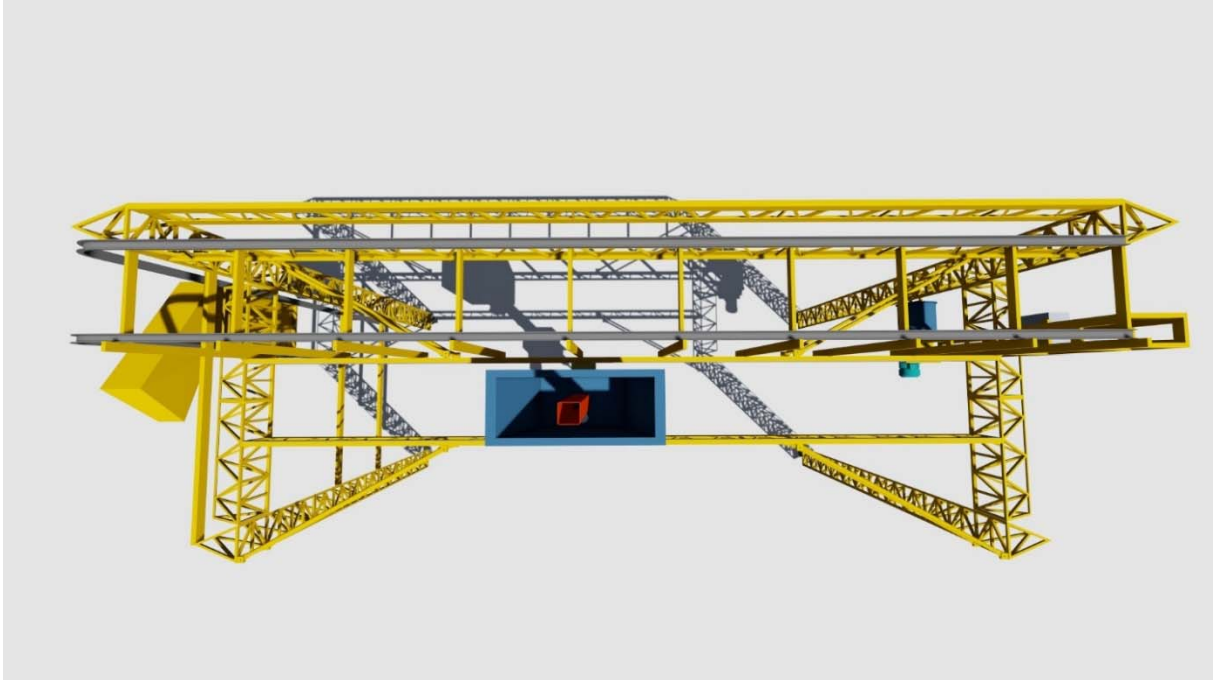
30. Impresora de coordenadas rectangulares con estructura aporticada. Vista en planta
